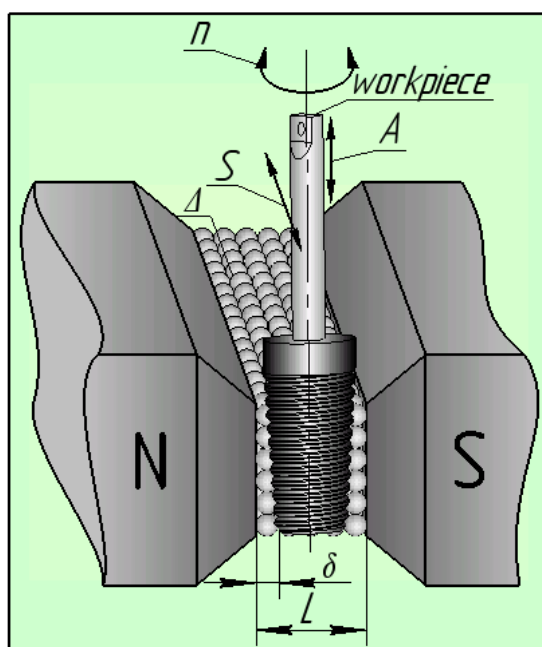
Схемы магнитно-абразивной обработки наружных и внутренних резьбовых поверхностей
